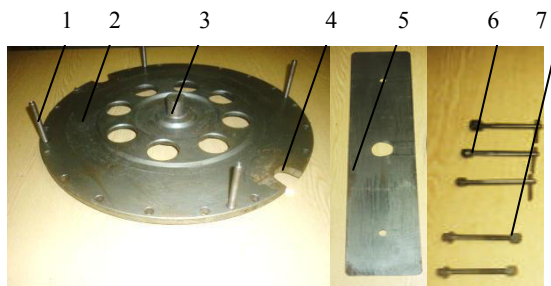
Кондуктор для сборки главного фрикциона:
